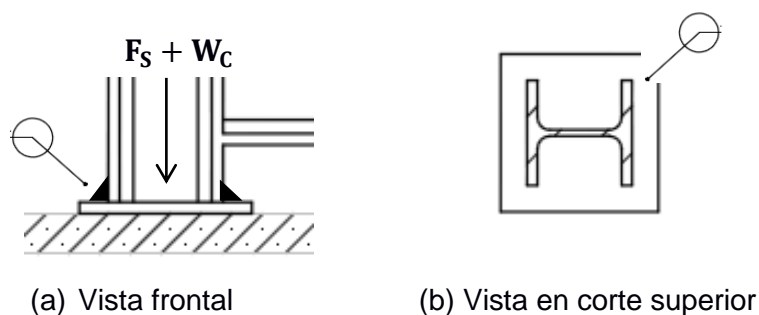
Fuerzas presentes en la unión de soldadura #3.
